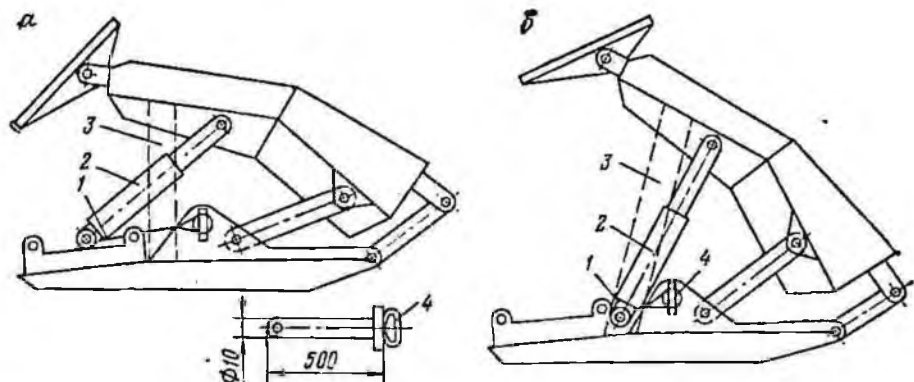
Схема подъема перекрытия секции крепи сопряжения Т6К:
